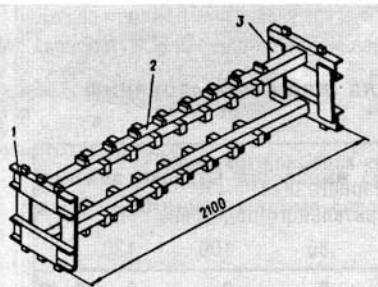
Сварная конструкция рамы в сборе: 1 – деталь боковой рамки; 2 – балка со скобами и упорами; 3 – боковая рамка в сборе
